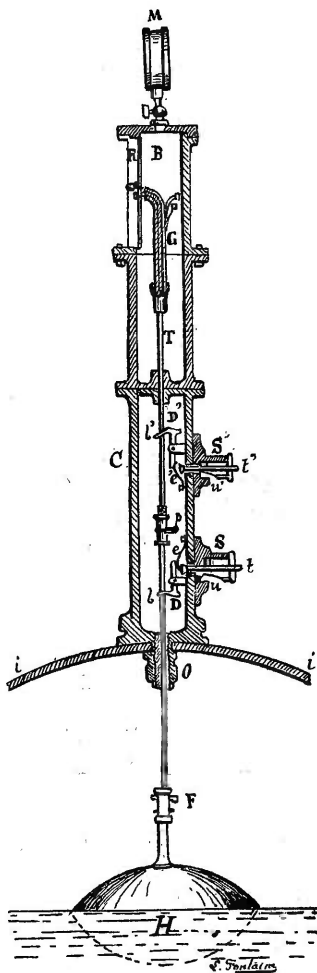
Coupe de l'indicateur magnétique (Lethuillier et Pinel).
